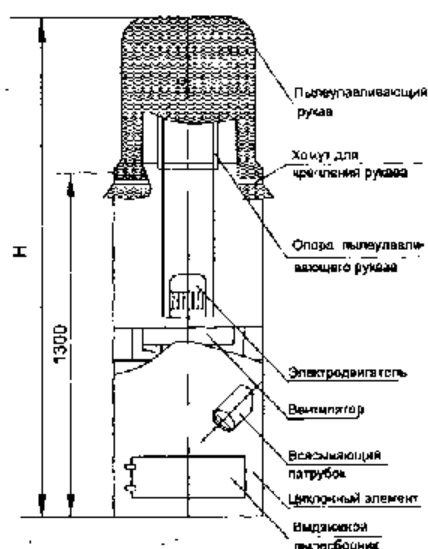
Пылеулавливающий агрегат АПР
